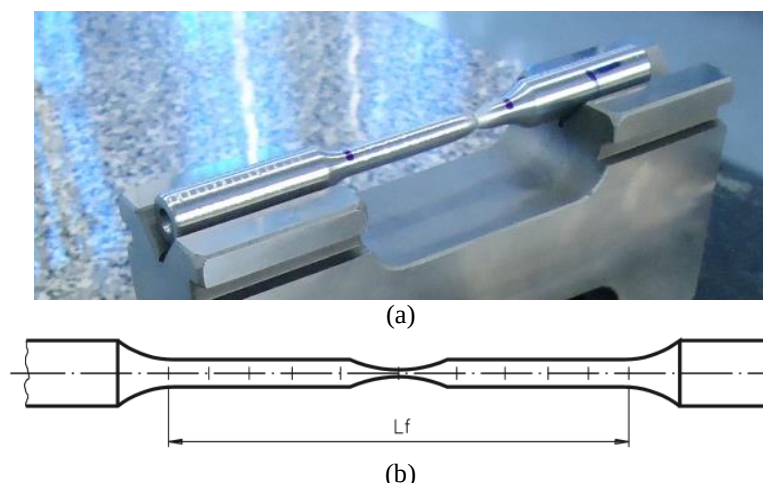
(a) Medição do alongamento, (b) Corpo de prova depois do ensaio de tração (Fundação Roberto Marinho, 2009)
